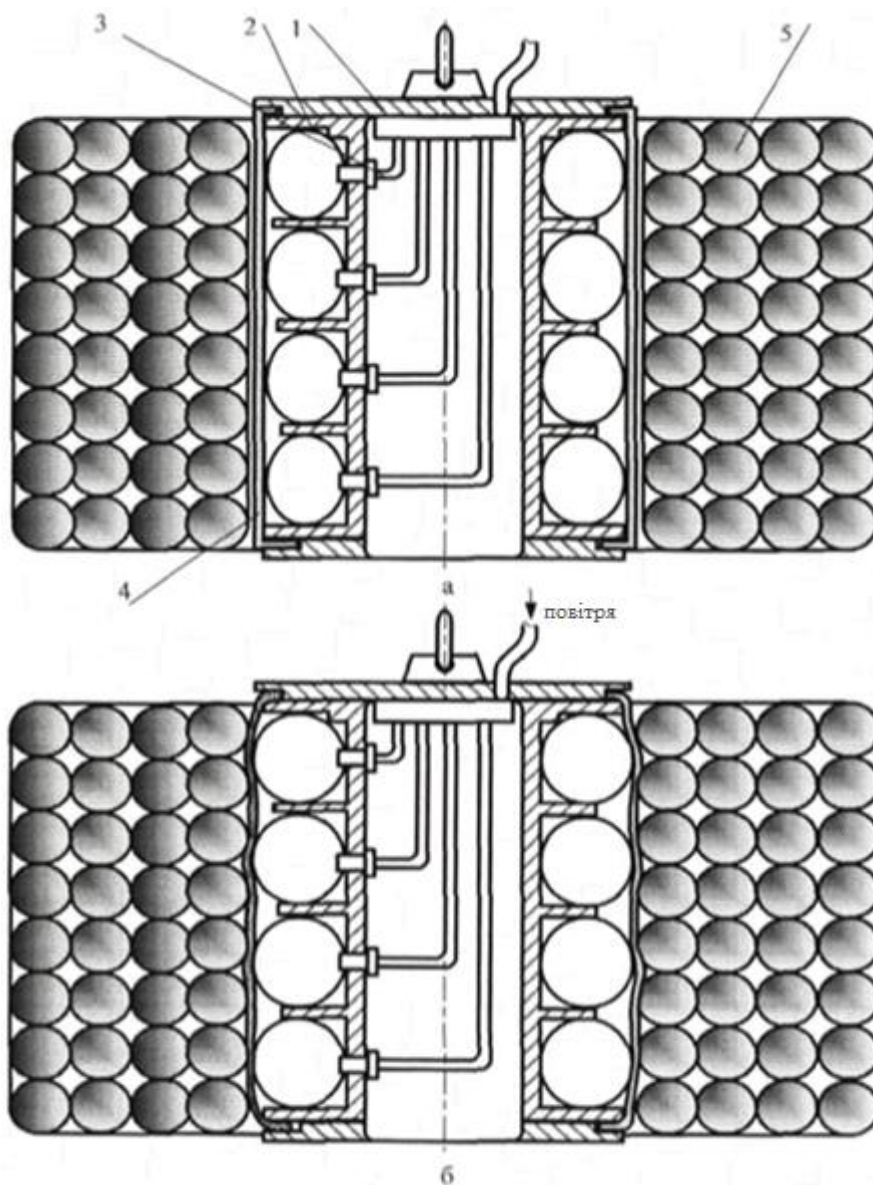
Схема багатокамерного захоплювального пристрою:
